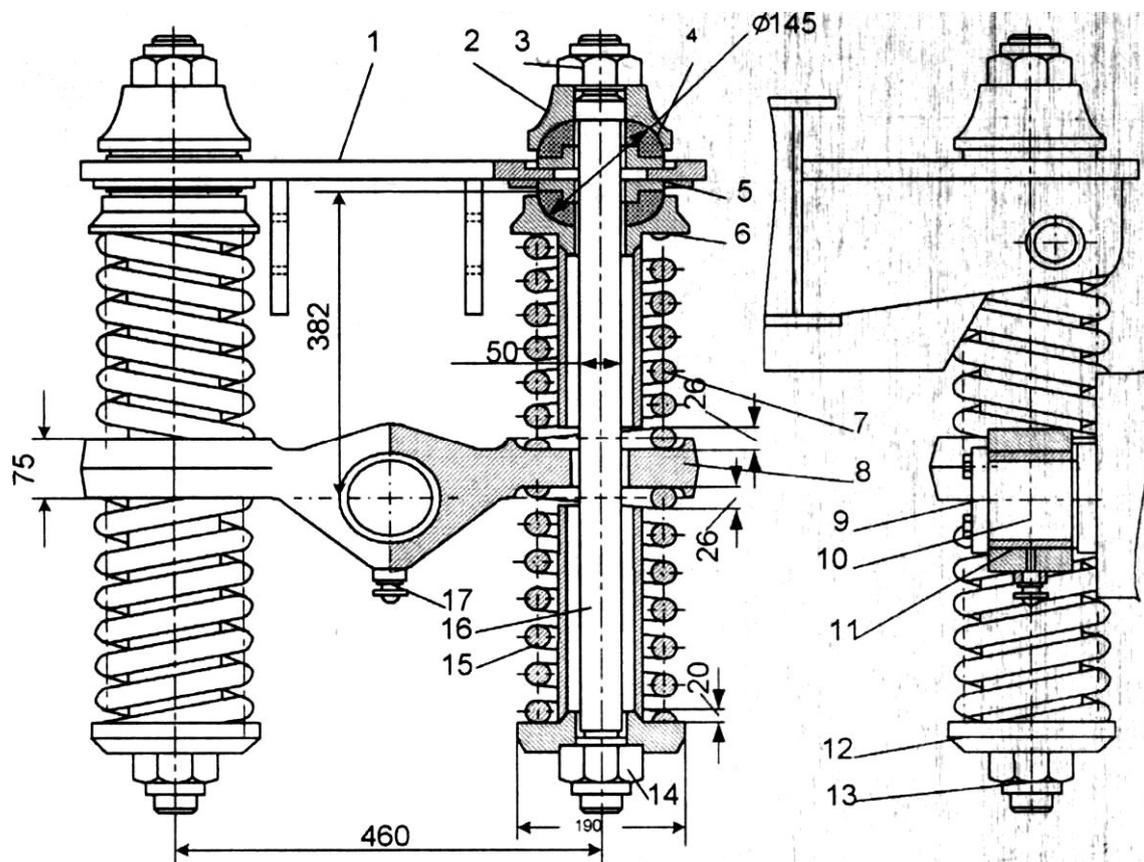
Люлочное подвешивание тягового двигателя: 1- кронштейн поперечной балки рамы тележки; 2-колпак; 3- корончатые гайки; 4,5-верхняя и нижняя полушферы; 6, 12- поддоны; 7, 15-верхние и нижние пружины; 8-баланси́р; 9- шайба; 10-цапфа; 11-втулка; 13-шплинт; 14-корончатые гайки; 16-подвески, 17-масленка
